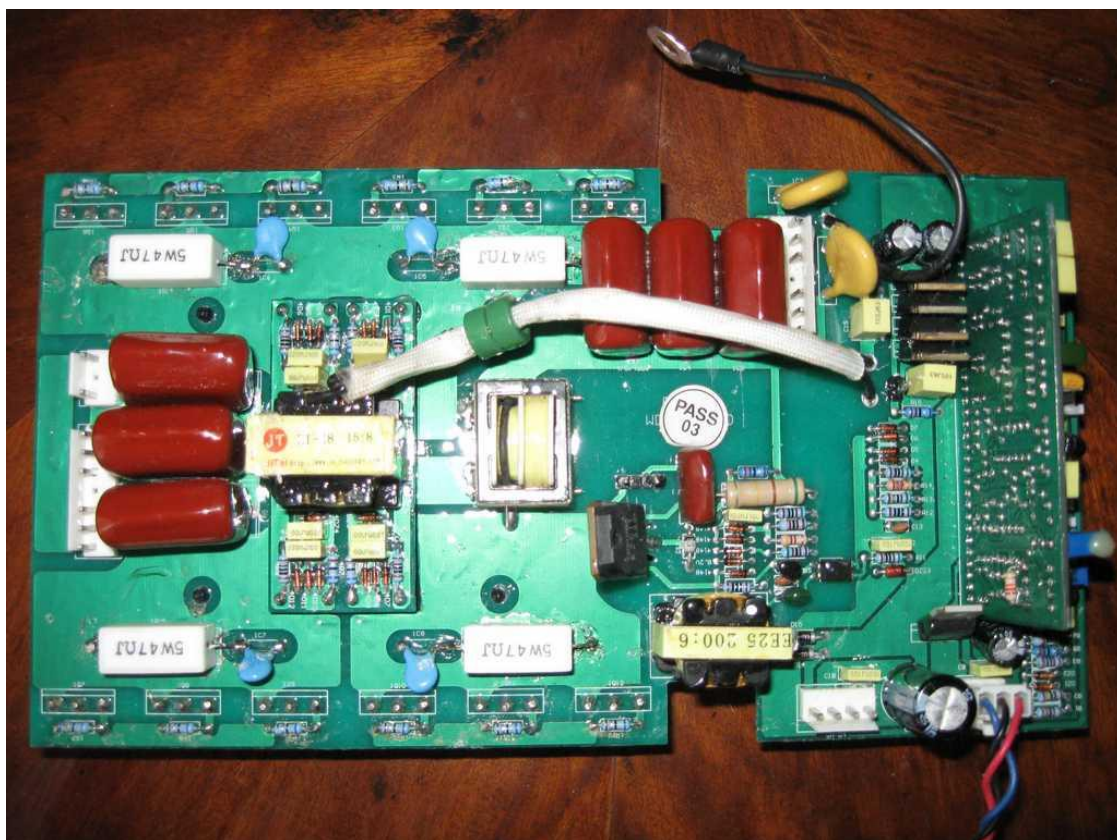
Внешний вид компоновки инвертора Ресанта.
